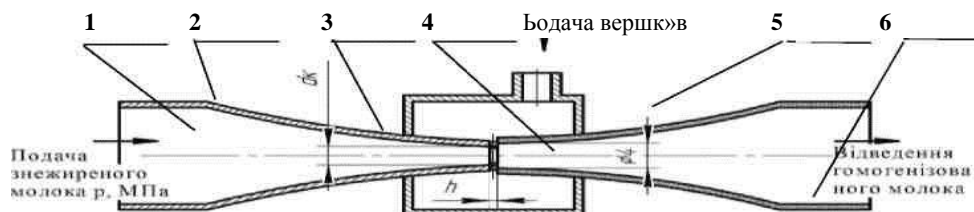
Схема робочої камери щілинного гомогенізатора молока струминного типу
